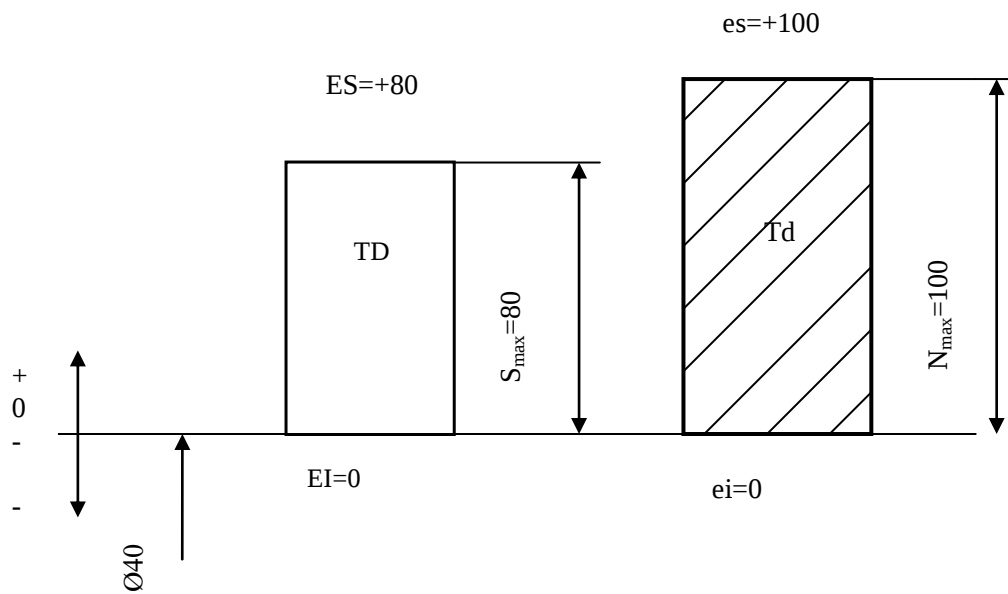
Схема розташування полів допусків деталей з'єднання
